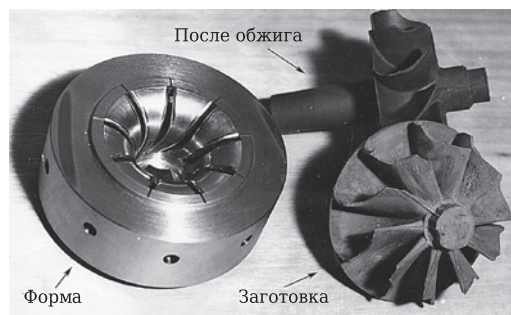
Керамическое колесо турбокомпрессора из нитрида кремния
